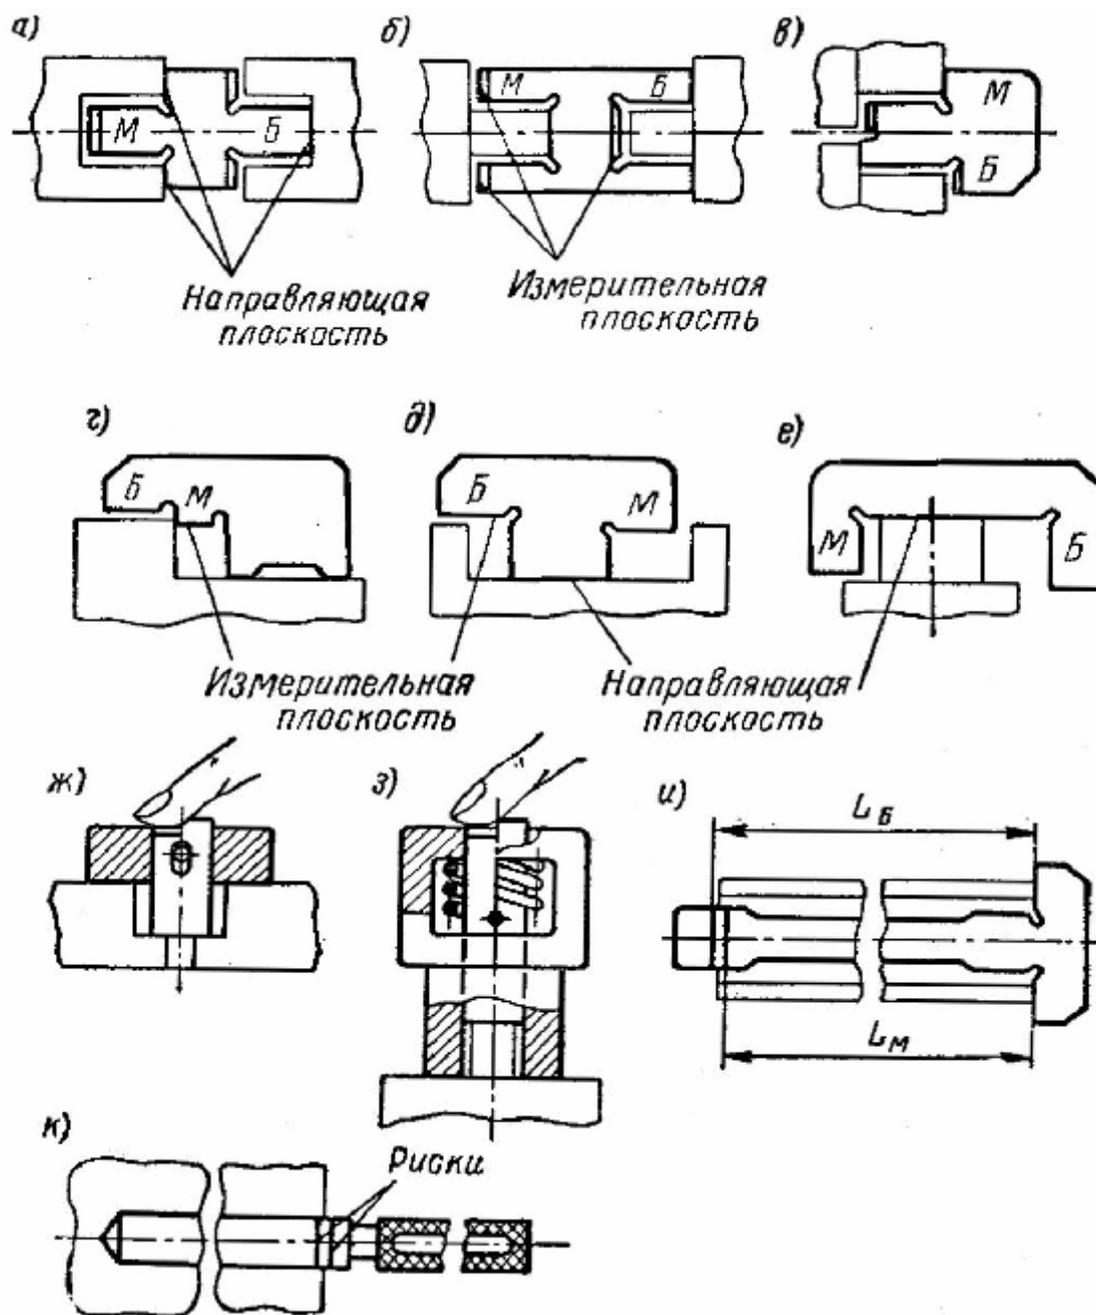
Конструкция и типы калибров для контроля размеров глубин и высот уступов
